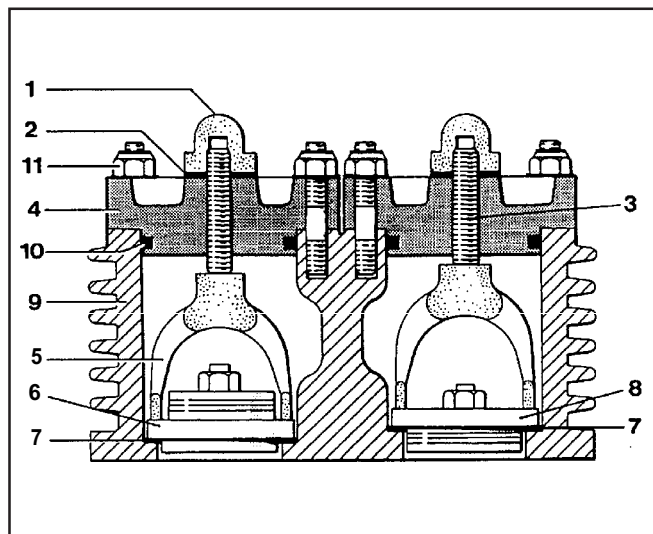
Головка клапана и клапаны, 1-я ступень К180
